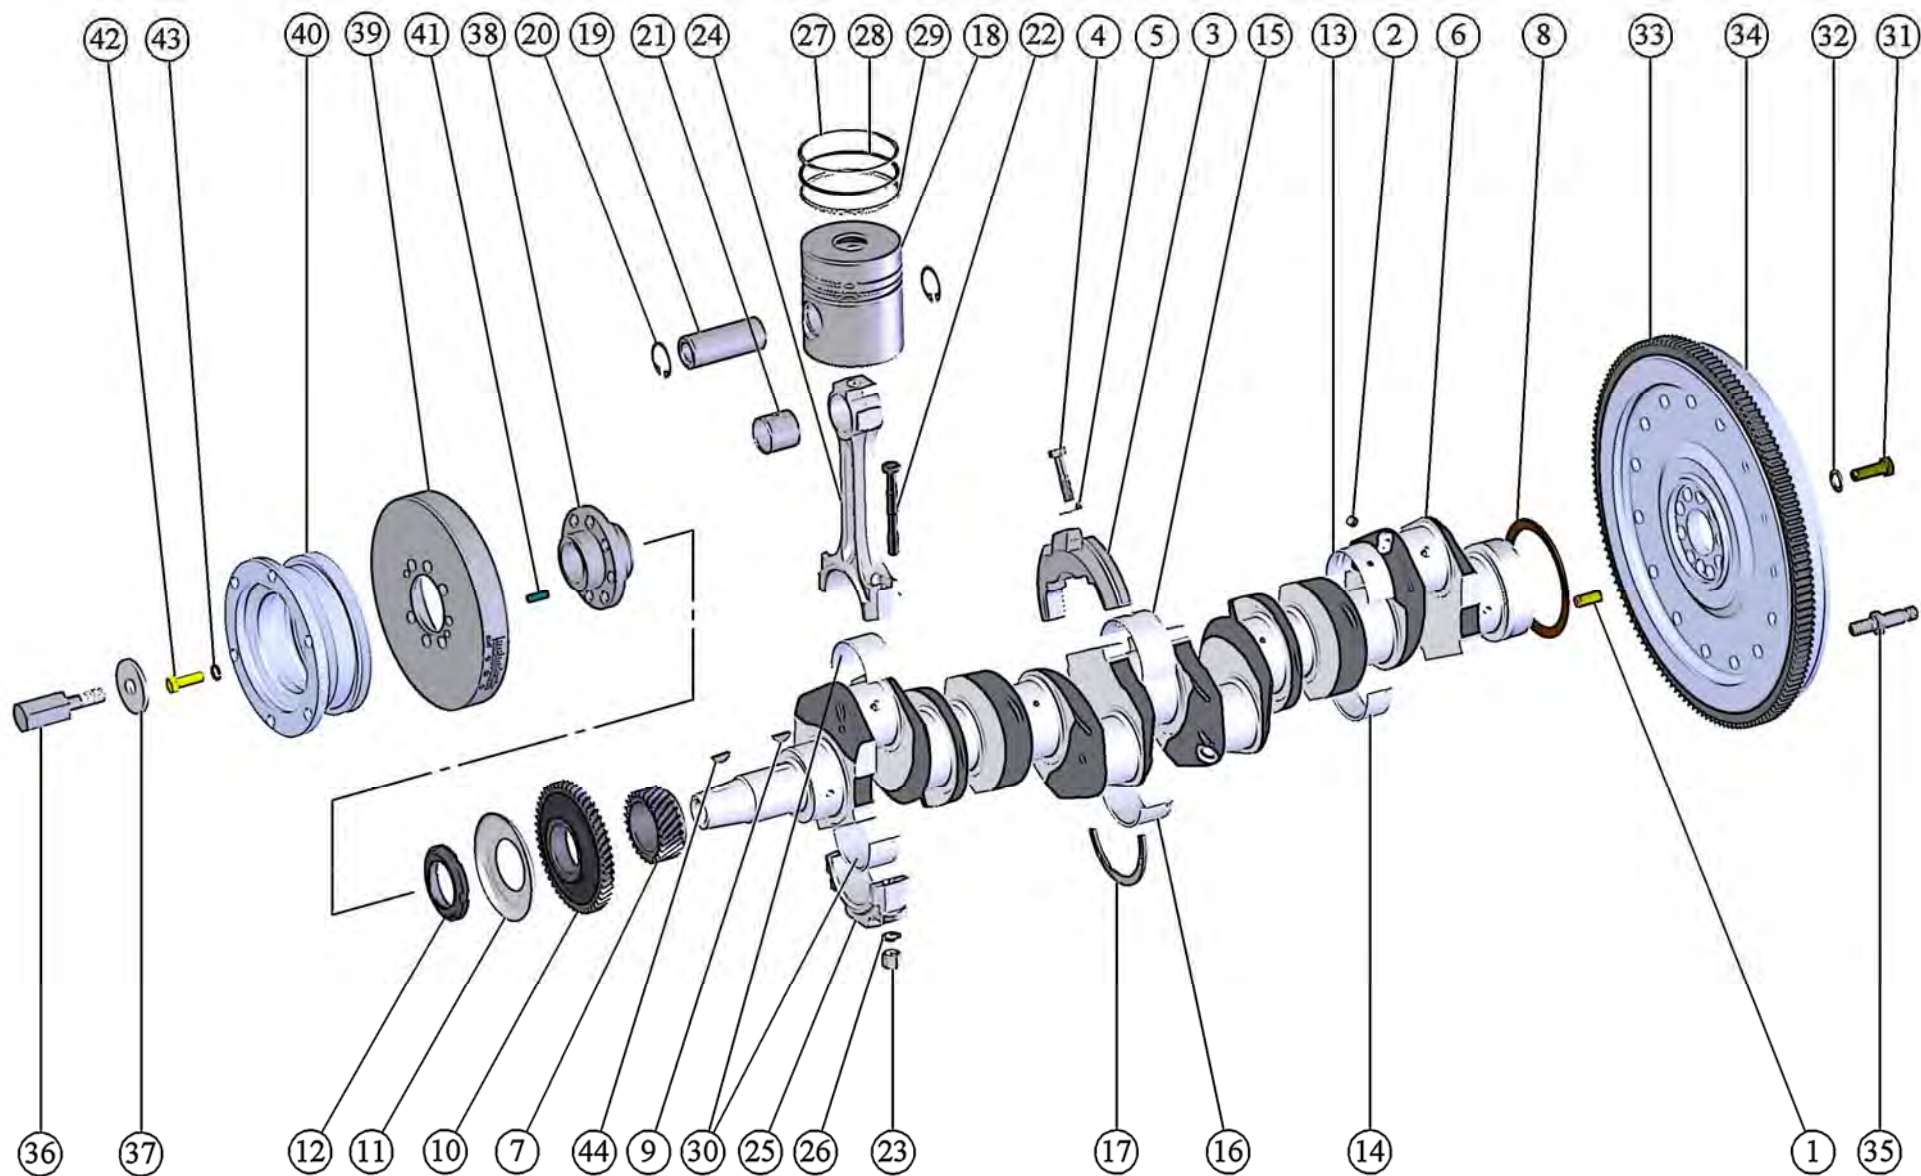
Кривошипно-шатунный механизм. Установка маховика. Установка шкива коленчатого вала.
